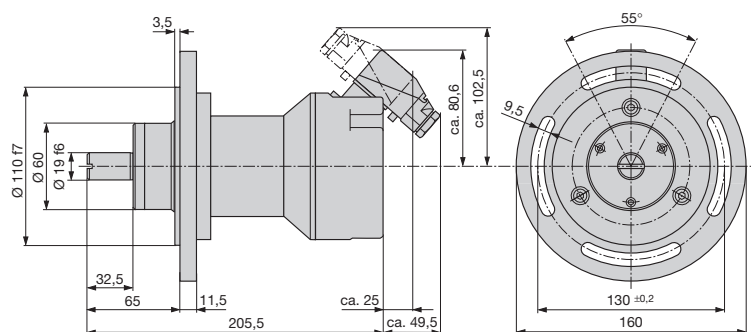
KINAX WT 707 mit Zusatzgetriebe, Steckverbinder und Flansch.
